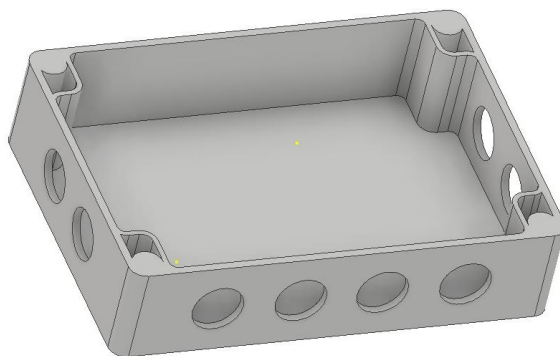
Варианты расположения кабельных вводов при монтаже на плоское основание (стенку)
